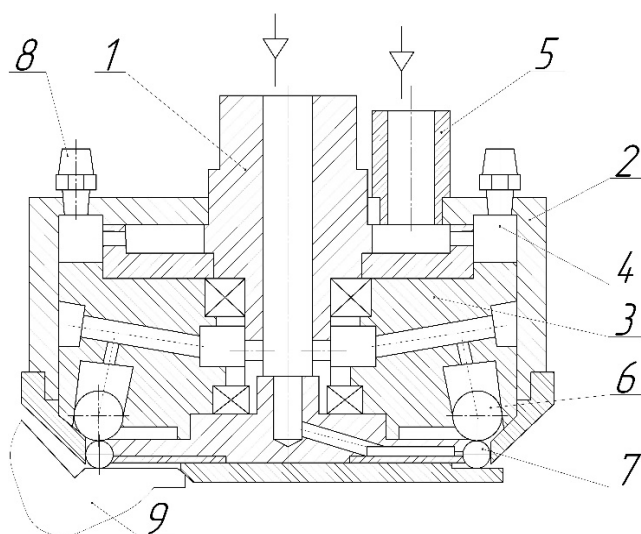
Конструкция инструмента для упрочняющей обработки пневмоударом плоских поверхностей: 1 – полый вал; 2 – корпус; 3 – диск; 4 – лопатки; 5 – штуцер; 6 – приводящие шары; 7 – деформирующие шары; 8 – пневмоглушители; 9 – заготовка
